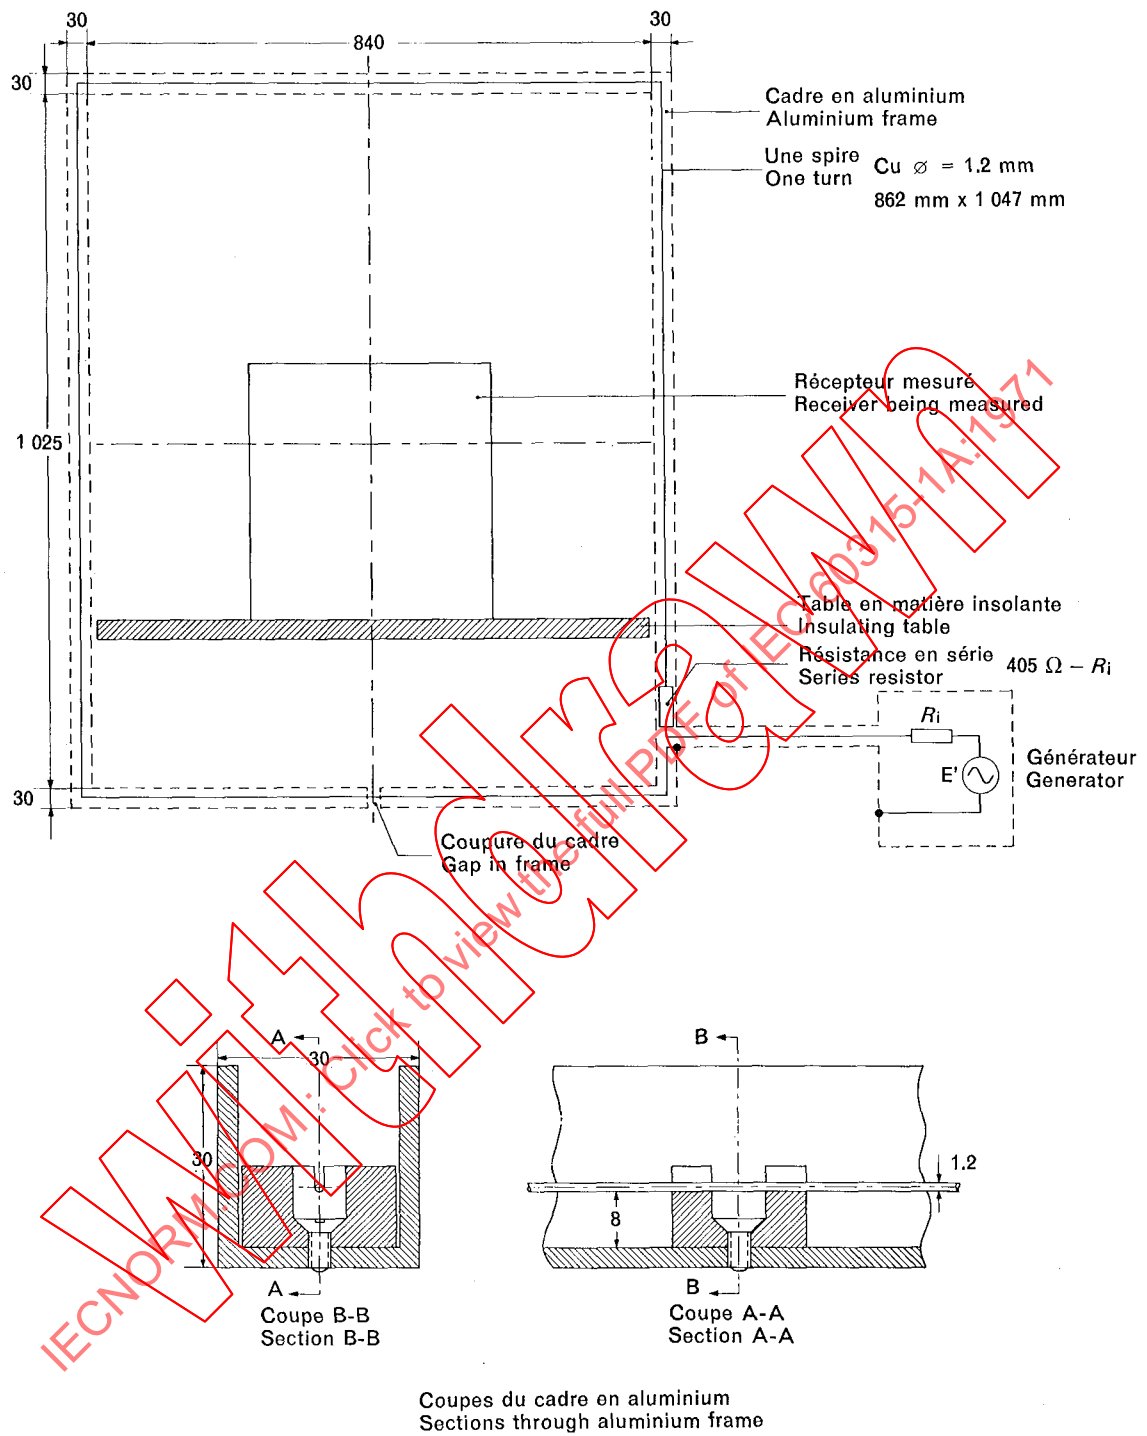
Cadre de moyennes dimensions, partiellement blindé.
